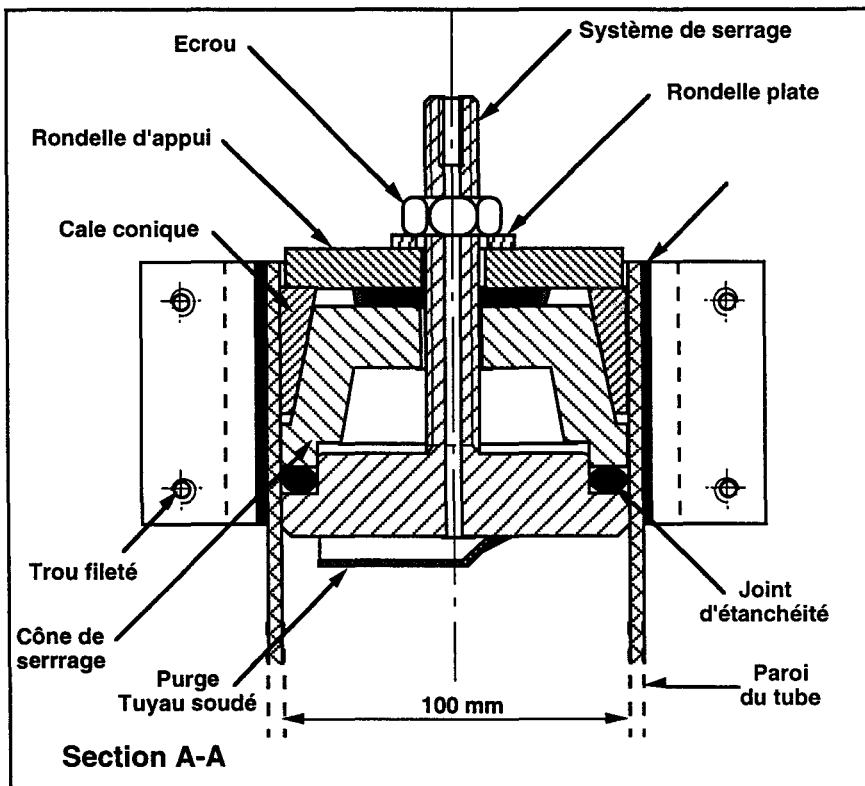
Systèmes d'étanchéité (bouchon) et de fixation des structures tube - Vue en coupe
